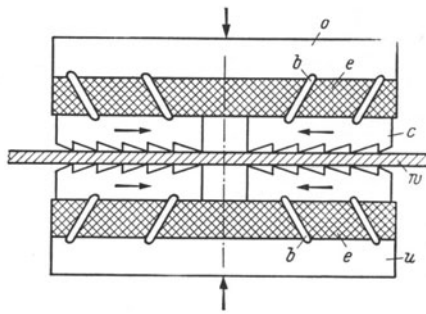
Stauchwerkzeug *Eckold-Verfahren
